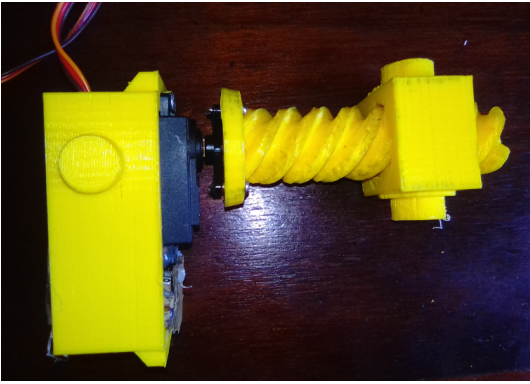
Servo-moteur attaché à côté de l'épaule
